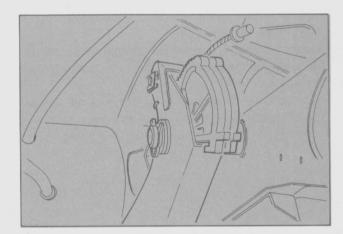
Desmontaje del cable de embrague del segmento dentado.
